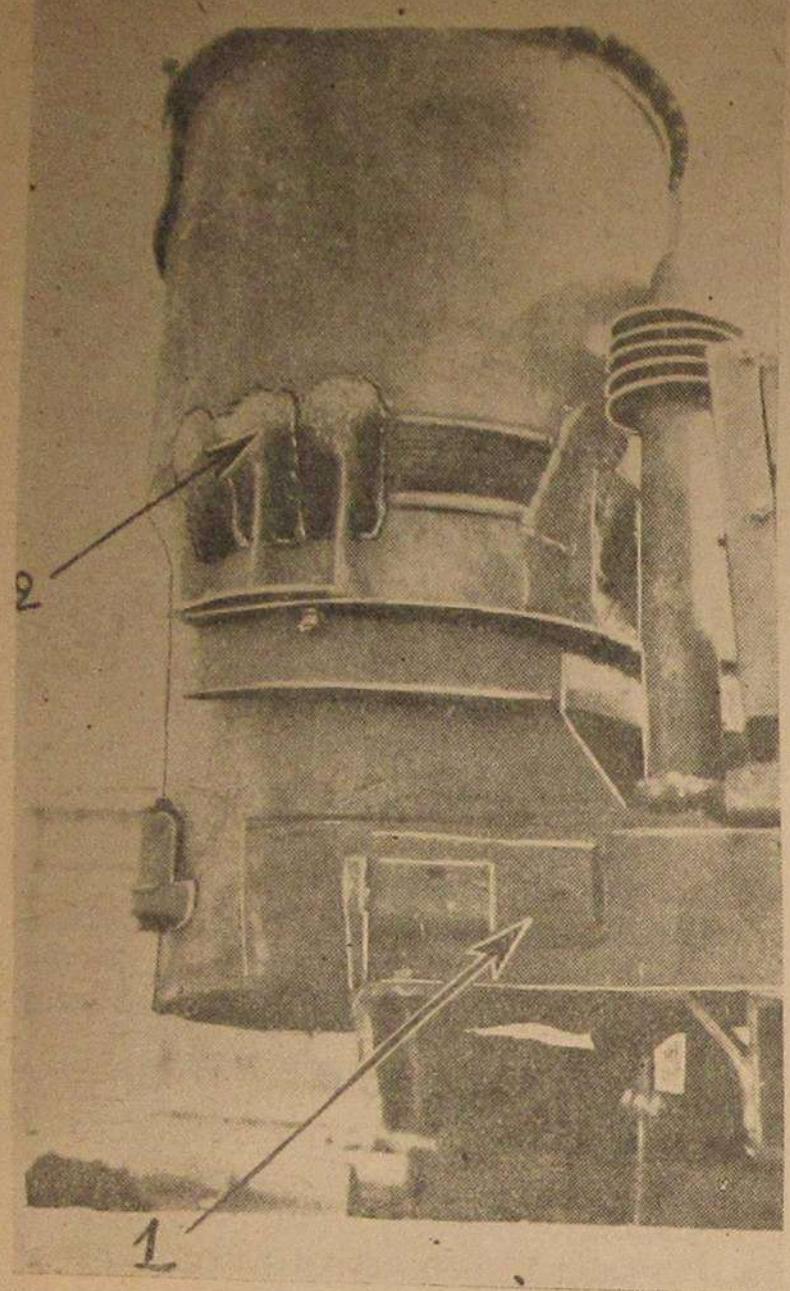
Способ устранения поломки рамы газогенератора ЛС-1-3 и обрыва ребер крепления бункера. 1. Наварка накладки для усиления рамы г/г. 2. Наварка заплат для усиления приварки ребер крепления бункера к раме.
